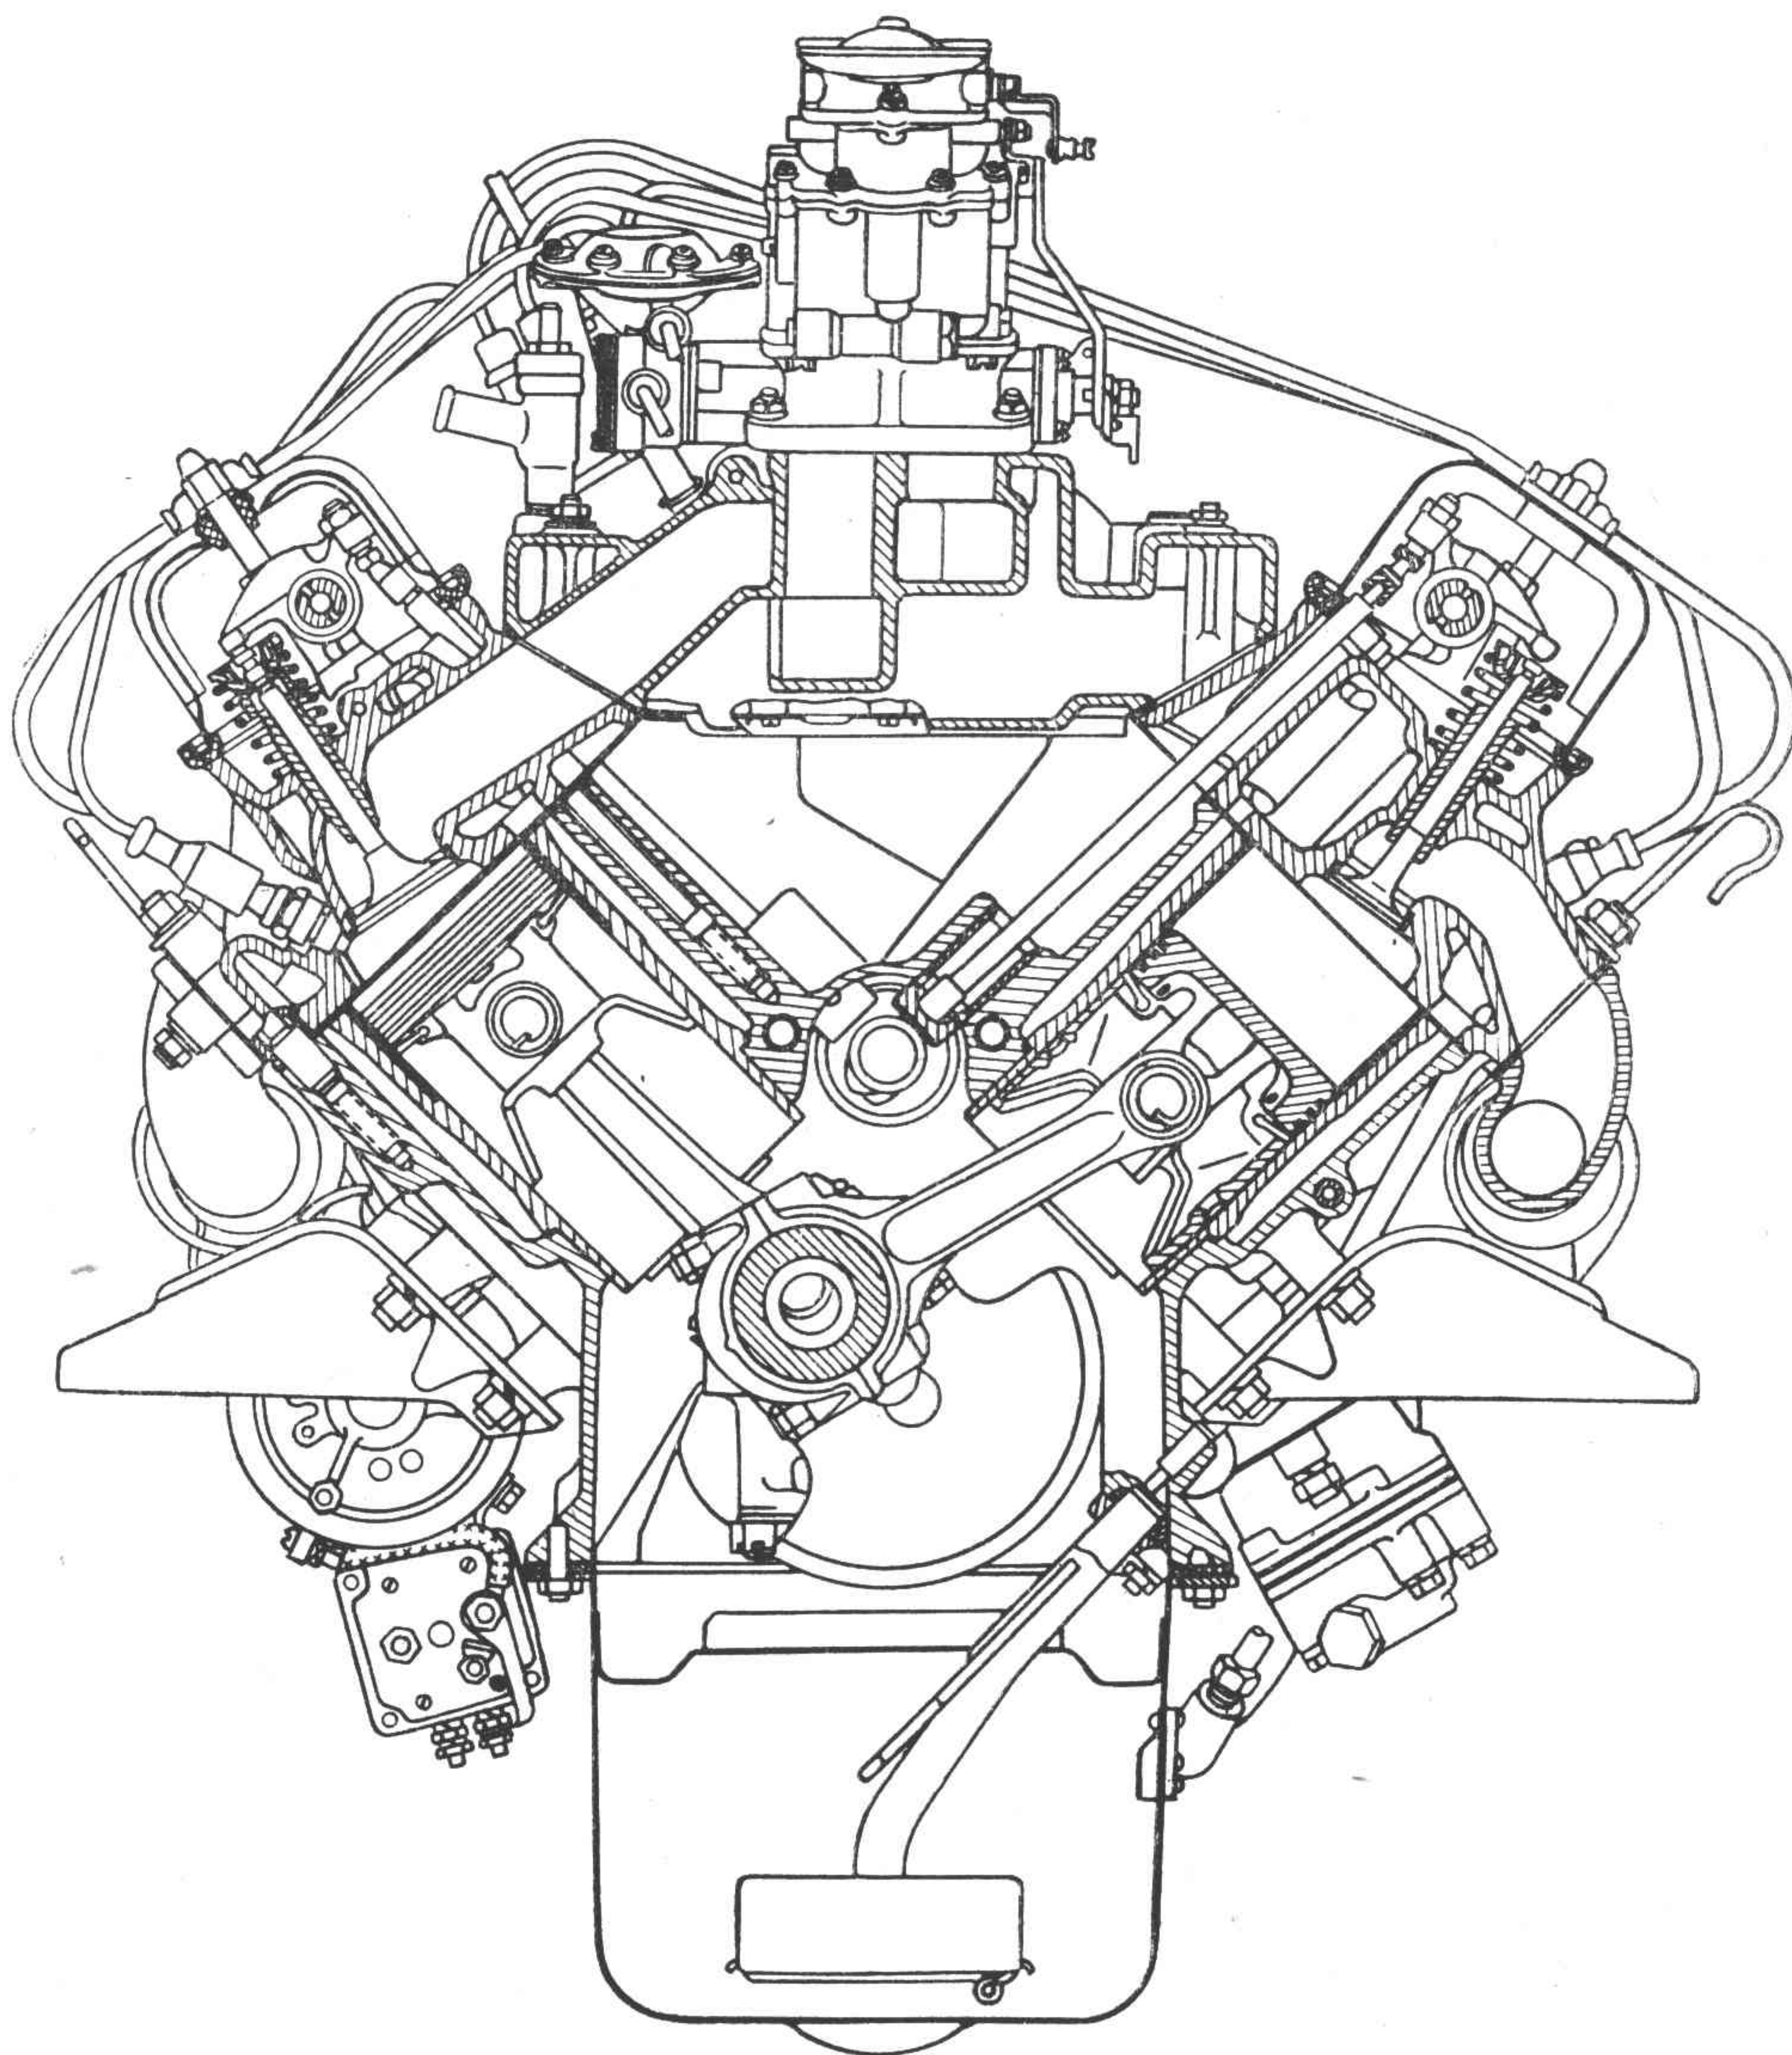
Поперечный разрез двигателя ГАЗ-66
